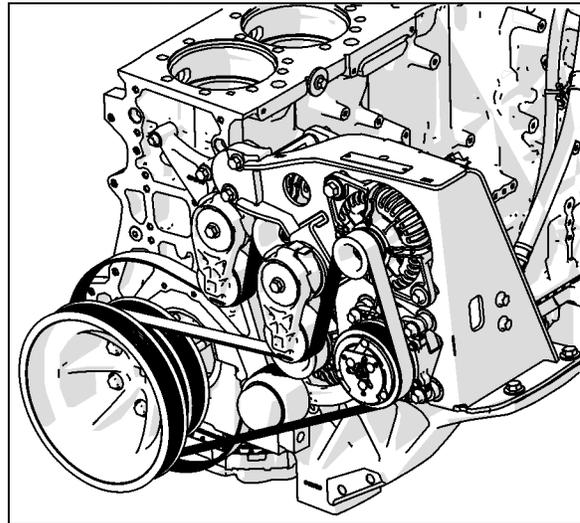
COMPRESOR DE A/C PEQUEÑO SERIE X3
